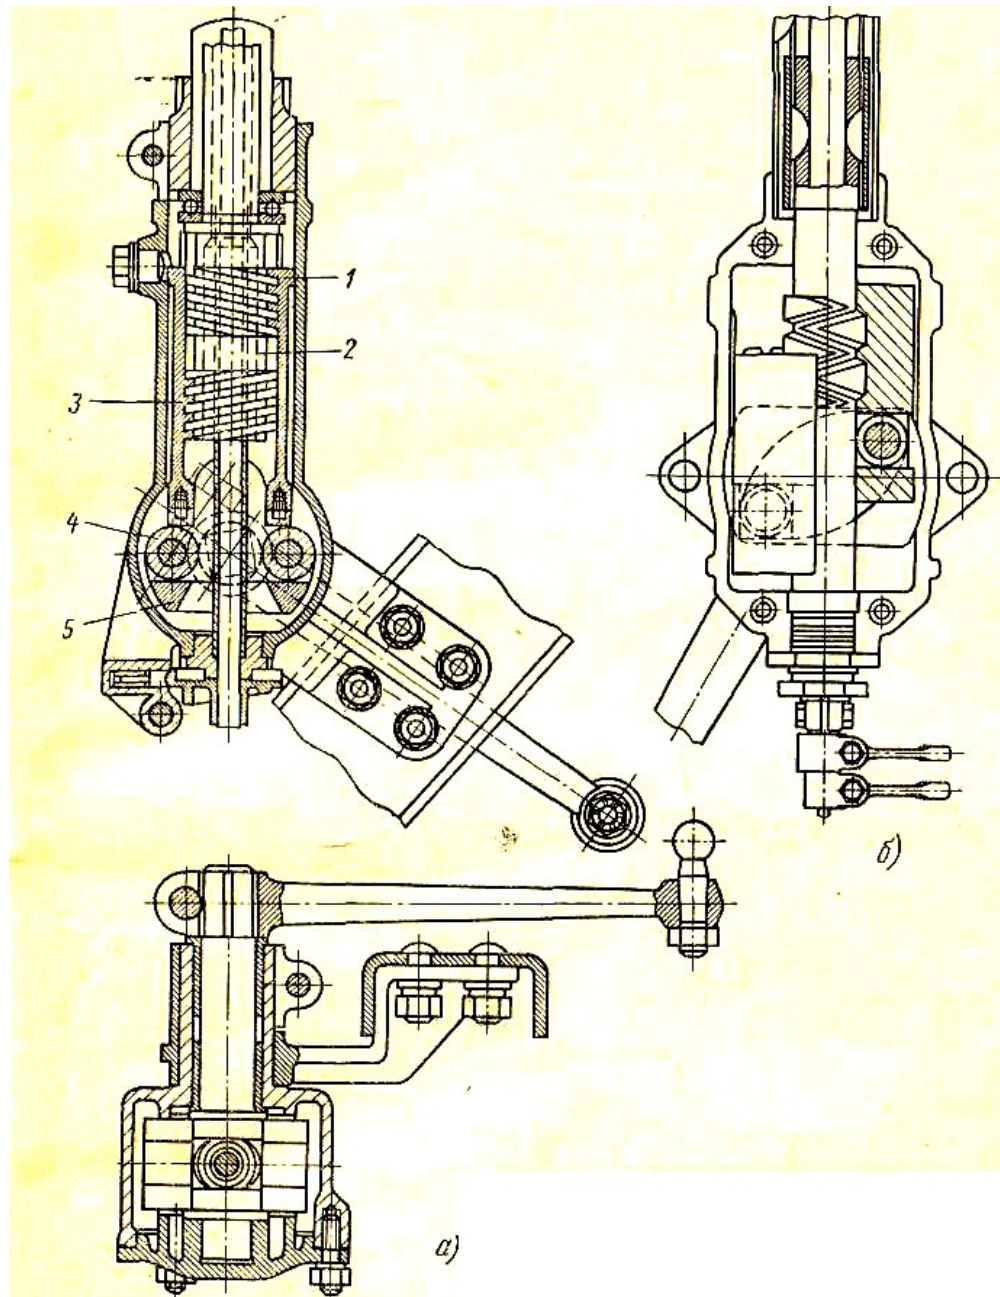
Рулевые механизмы с винтовой передачей, полугайками и двуплечим рычагом
